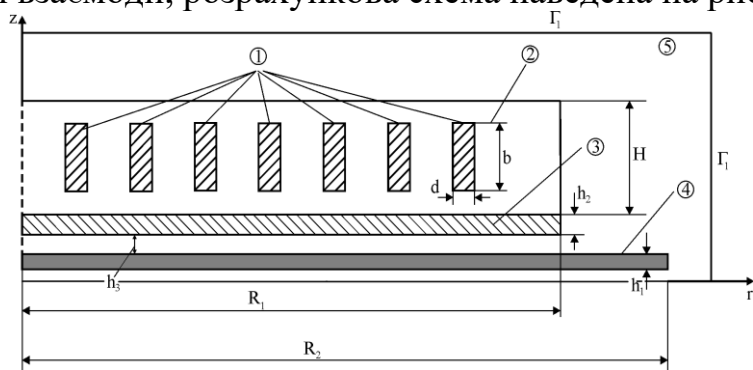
Складений багатовитковий індуктор із допоміжним екраном та заготовка: 1 – струмопровід; 2 – допоміжний екран; 3 – діелектричний бандаж; 4 – заготовка; 5 - повітря
